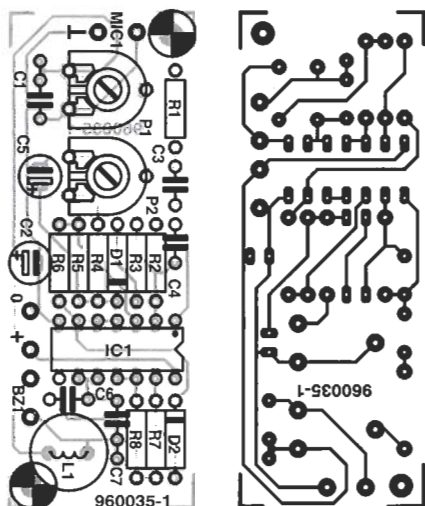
Las pequeñas dimensiones de la placa aseguran que el aparato sea muy pequeño.
